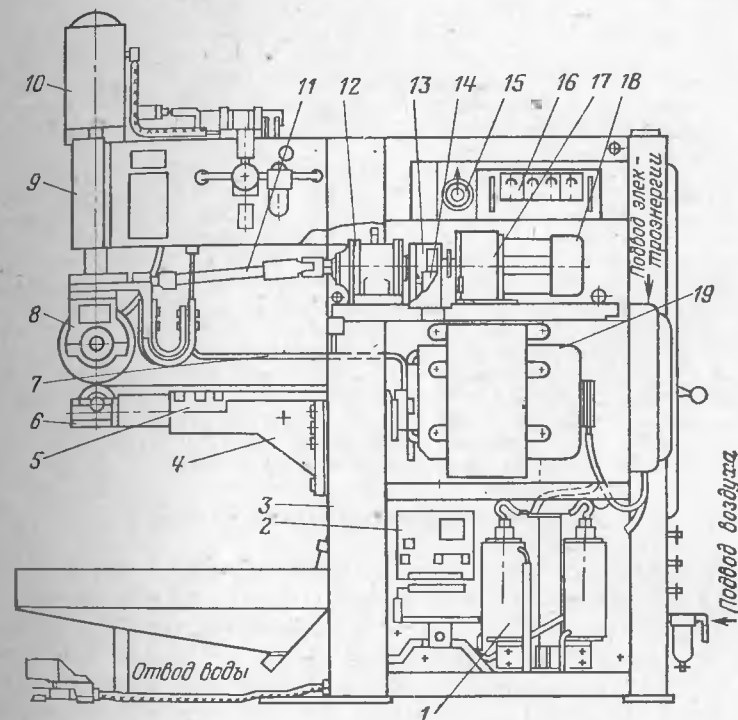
Машина для шовной сварки МШ-3201.
